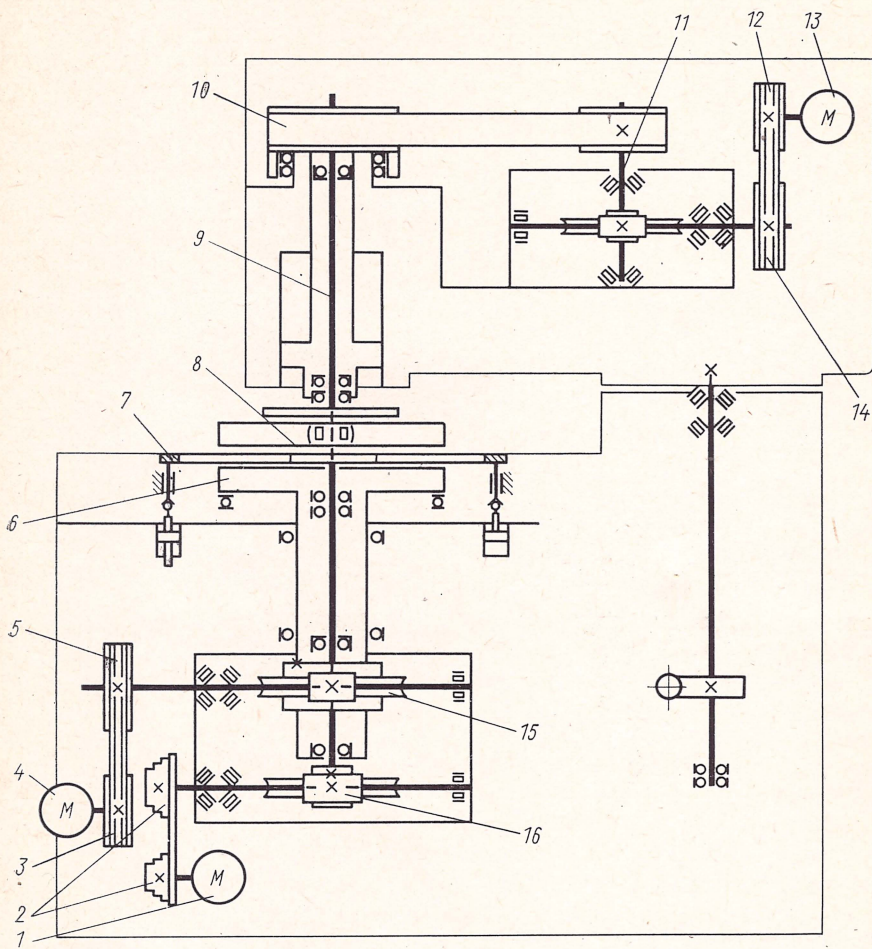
Кинематическая схема универсального вертикально-доводочного станка 3Д817
